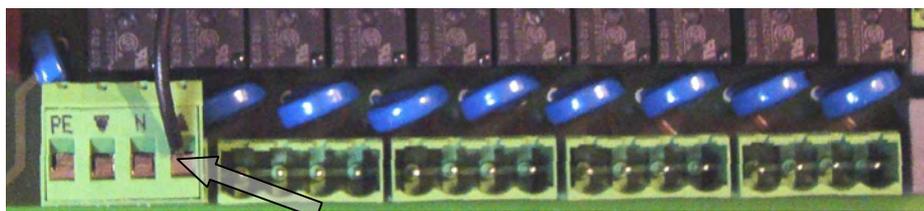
Detail 2 → Kabel mit Stecker am Block 5 verbinden
